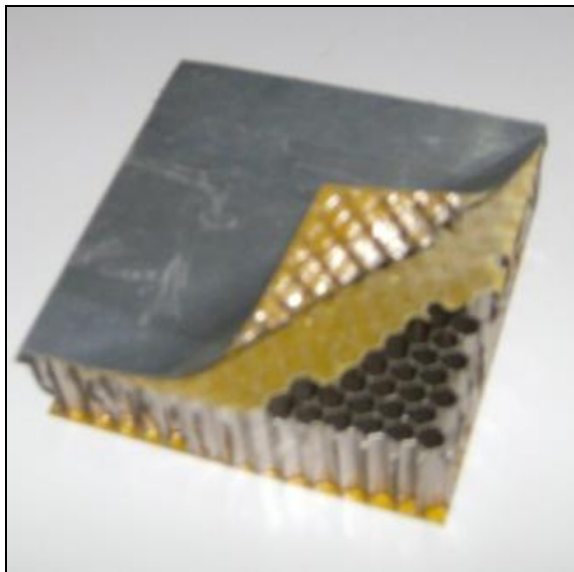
Painel sanduíche-colméia seccionado utilizado no satélite CBERS-2B.
